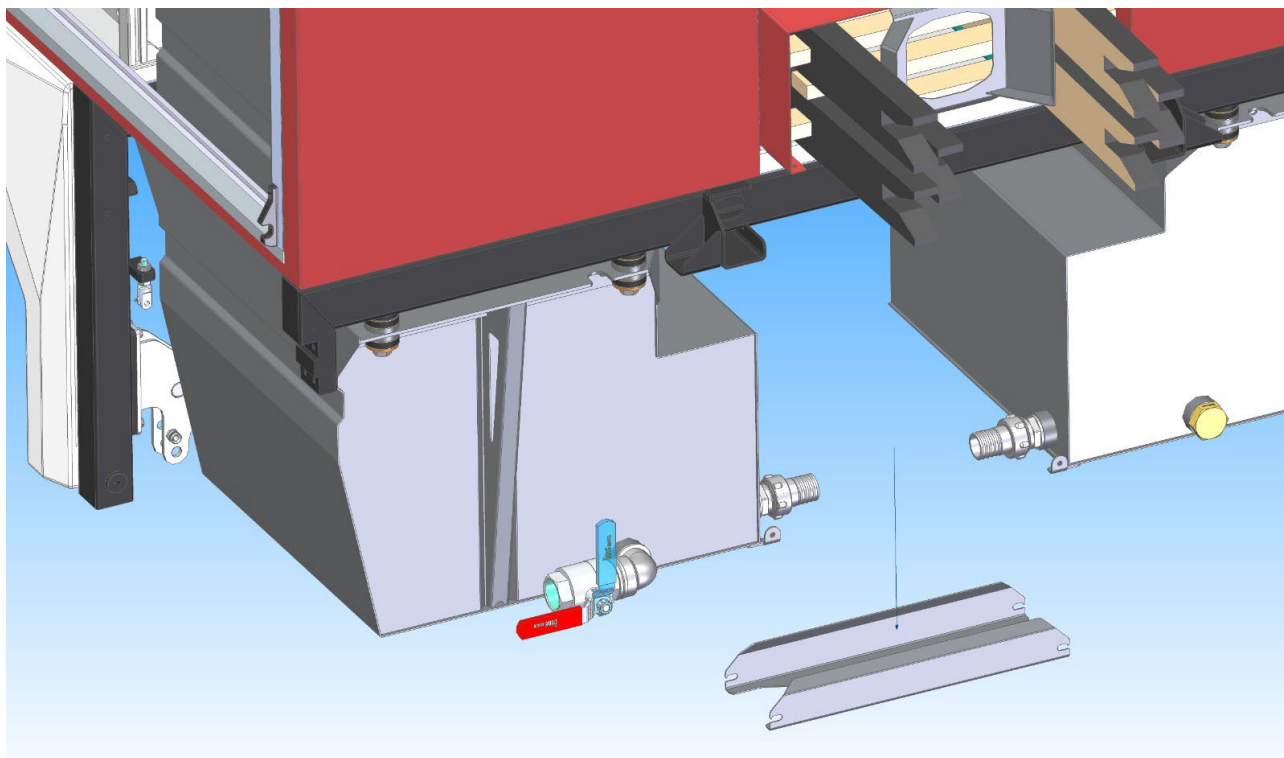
Rimozione carter di protezione e tubatura di collegamento
